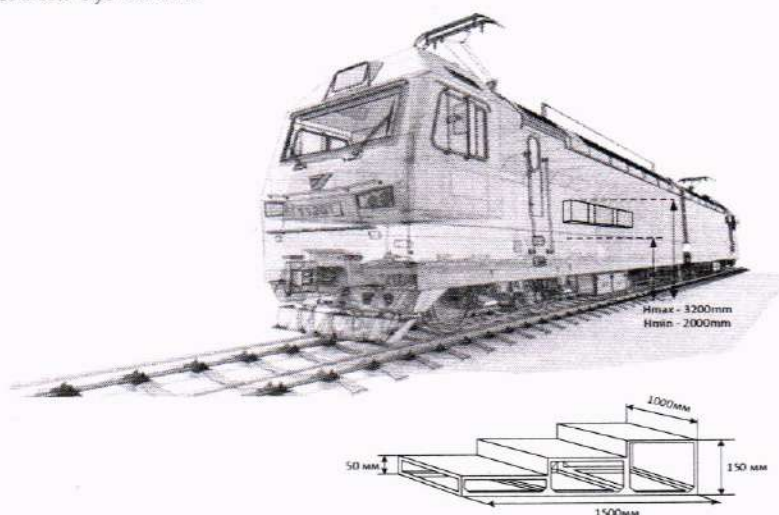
Размещение имитатора для проверки модулей ЛКПС ТРМЕ.441589.080 на борту локомотива и его габаритные размеры.
